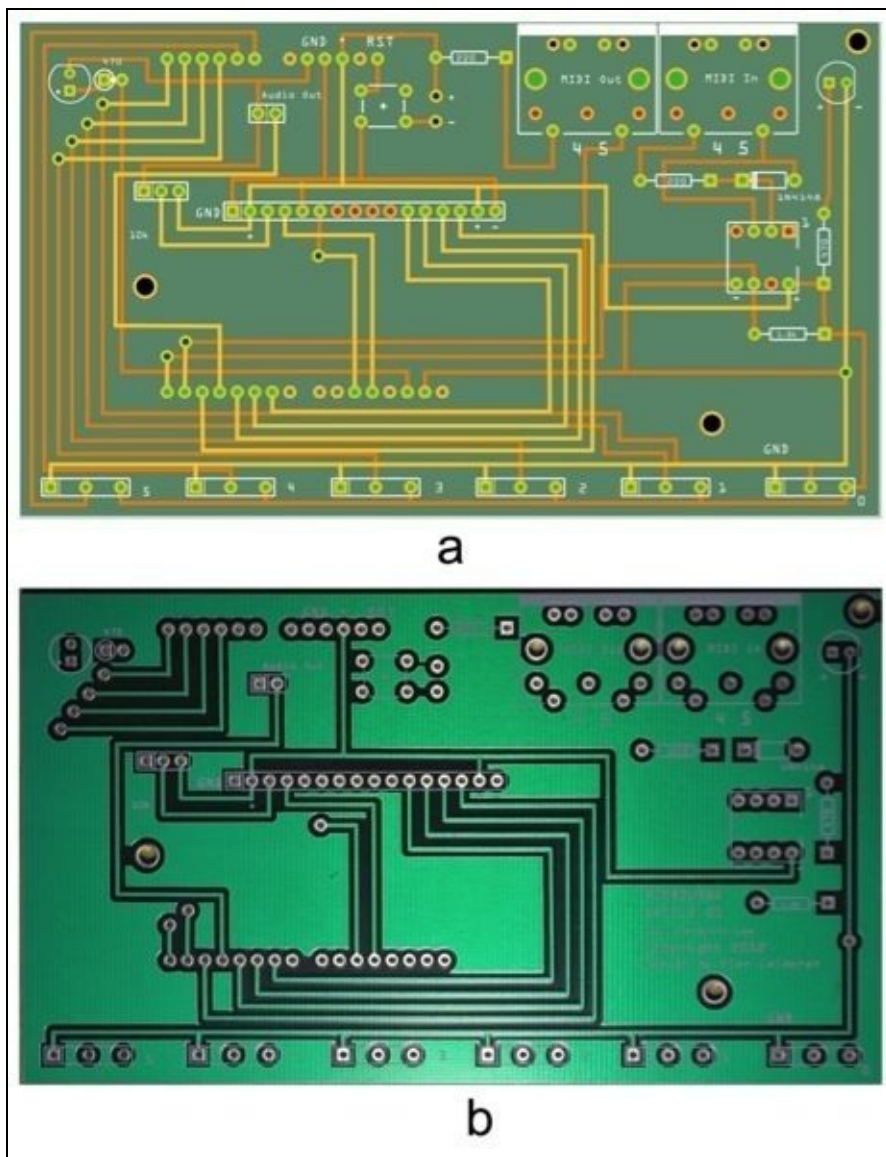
Layout virtuale con Fritzing di uno shield su PCB (a). Lo shield reale su circuito stampato autoprodotta (b).
